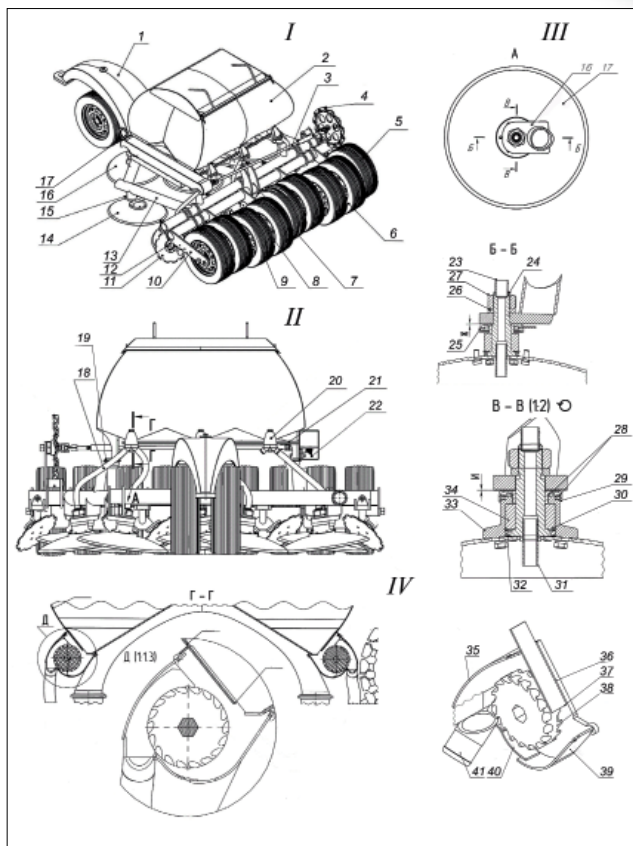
Электронная модель сеялки: I – вид сверху; II – вид спереди; III – узел крепления режущего диска; IV – высевающий аппарат; 1 – цепка; 2 – бункер; 3 – карданный вал; 4 – диск привода высевающего аппарата; 5, 6 – колеса; 7, 8 – двуплечие рычаги; 9 – уши; 10 – траверса; 11 – разрыхлители; 12 – стойки; 13 – рама; 14, 16 – режущие диски; 15 – лапы; 17 – двуплечие рычаги; 18 – семяпроводы; 19 – пятки для амортизаторов; 20 – высевающий аппарат; 21 – шестигранный вал привода; 22 – редуктор; 23 – ниппель; 24 – ось; 25, 29 – отбойник; 26 – шайба; 27 – гайка; 28 – сальник; 30 – стопорная шайба; 31 – разбрасыватель семян; 32 – сальник; 33 – корпус; 34 – подшипник; 35 – верхние подпружиненные дверки; 36 – щека; 37 – окна для выхода семян; 38 – дозатор; 39 – нижние подпружиненные дверки; 40 – пандус; 41 – разделитель
